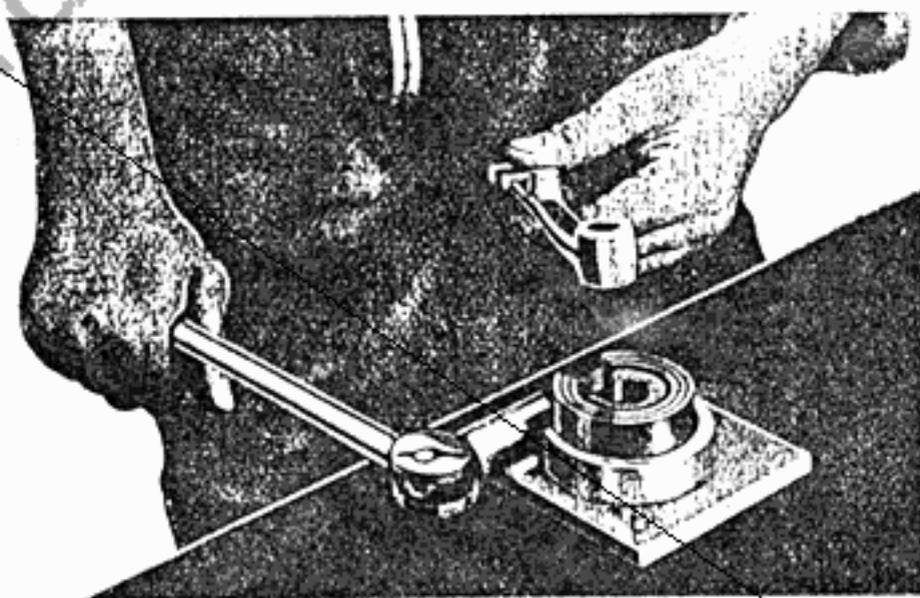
Rimontaggio gruppi sospensione anteriore
